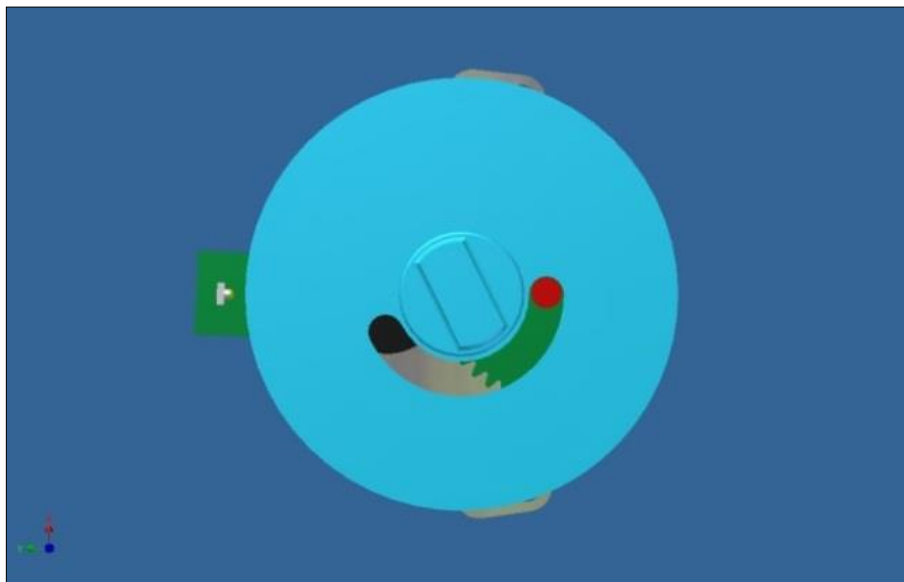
Secondo stopping point e vista in pianta dell'incavatura
